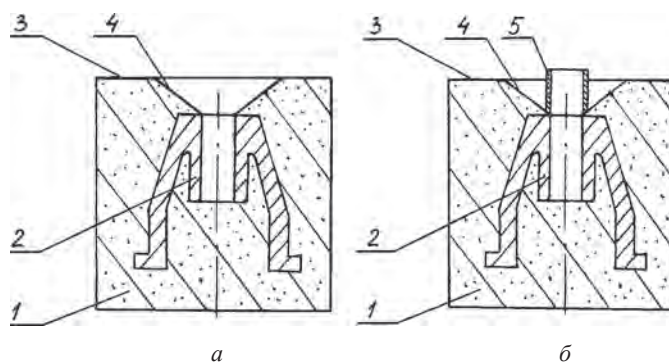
Литейная форма: в разрезе по оси цилиндра отливки (а); то же с патрубком, установленном на отливке (б): 1 – песок; 2 – цилиндр (гильза) отливки блока цилиндров; 3 – контрлад; 4 – естественный откос песка; 5 – патрубок
